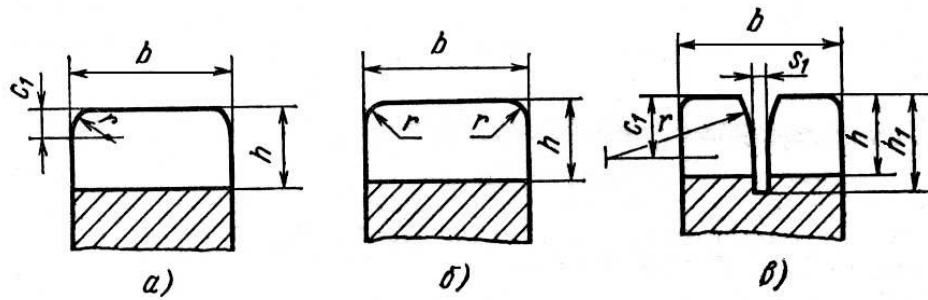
Форма поперечного профиля зуба звездочек зубчатых цепей
